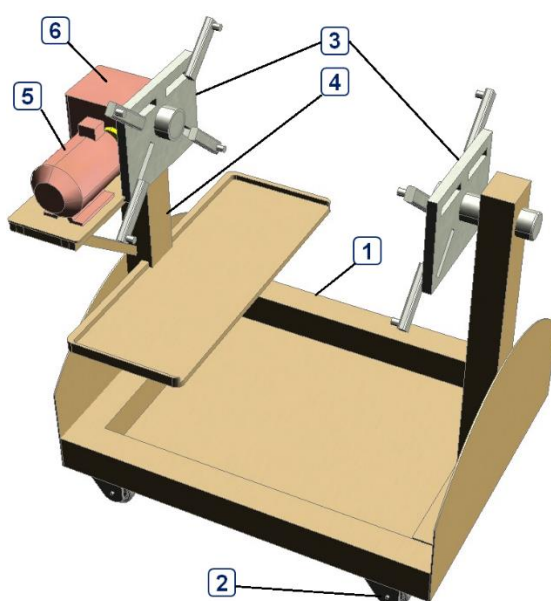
Трехмерная модель стенда: 1 - основание, 2 - ролики, 3 - планшайба, 4 - опора, 5 - электрический двигатель, 6 - червячный редуктор
